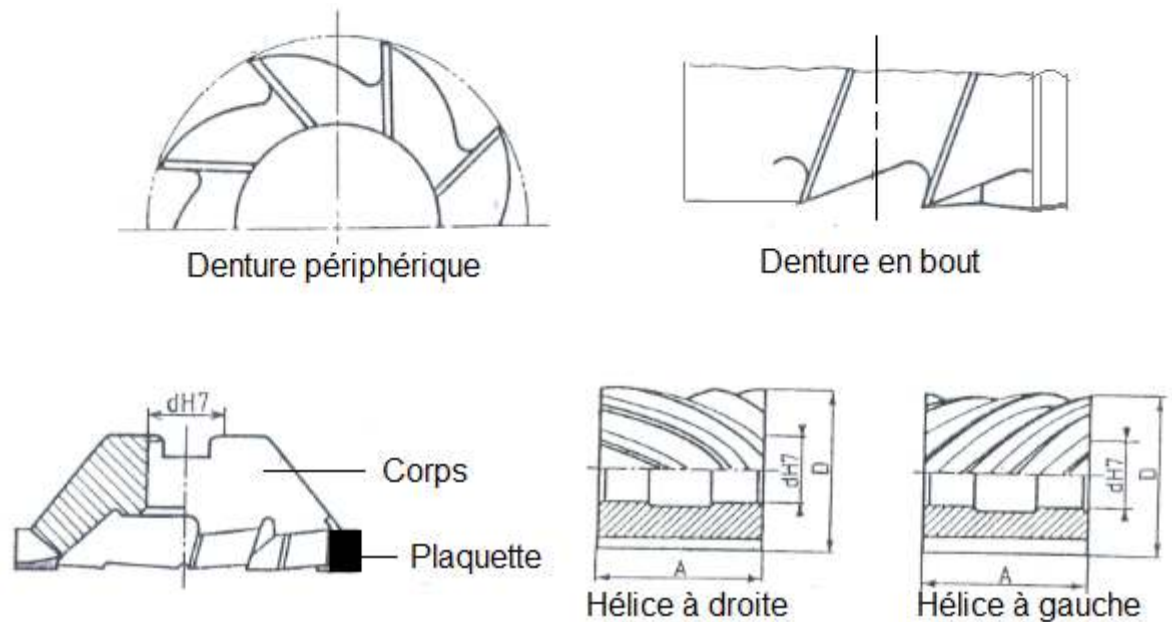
Type de fraises : en acier rapide ou en plaquettes rapportées en carbure
